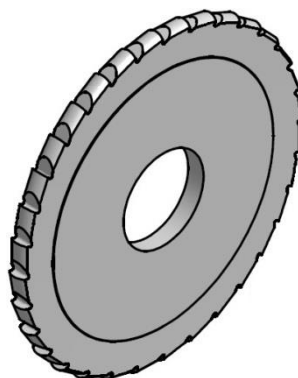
Geometria da fresa utilizada no processo de corte do *gap* de anéis de ferro fundido nodular, [Desenho TFV-008-07-4; MAHLE Componentes de Motores S.A.].
